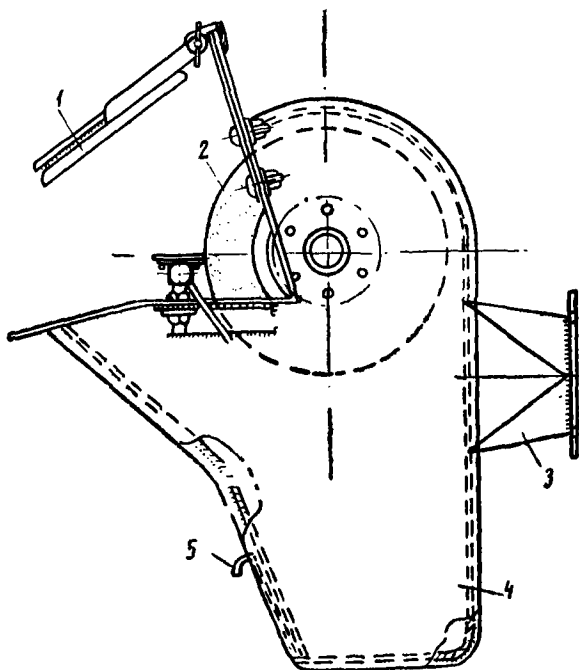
Защитно-обеспыливающий вытяжной кожух для станков ручной заточки инструмента:
